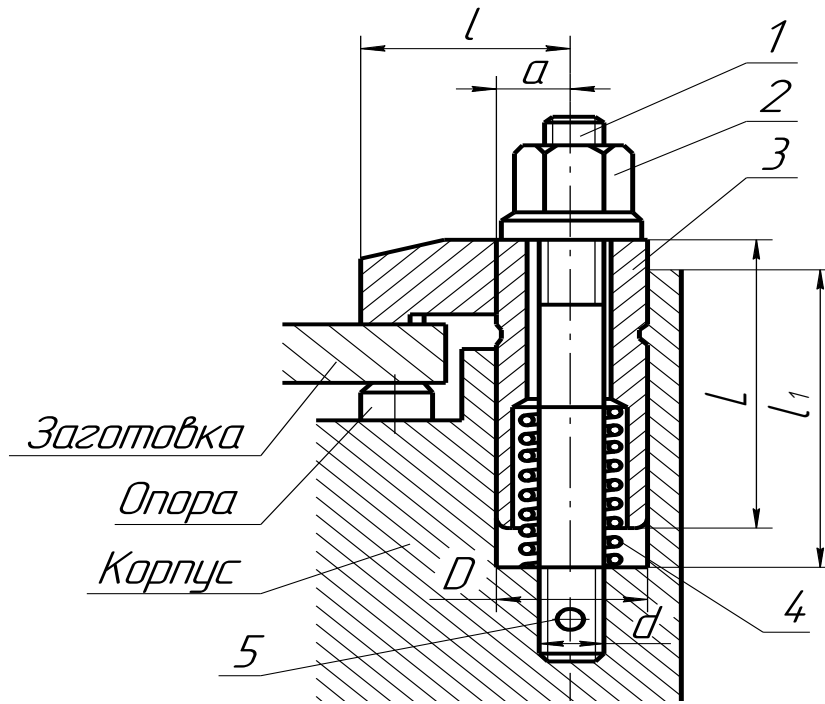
Конструкція Г - подібного комбінованого гвинтового ЗМ, що затискаються зверху. 1 - шпилька, 2 - гайка затискна, 3 – прихват Г- подібний, 4 - пружина, 5 - штифт.
